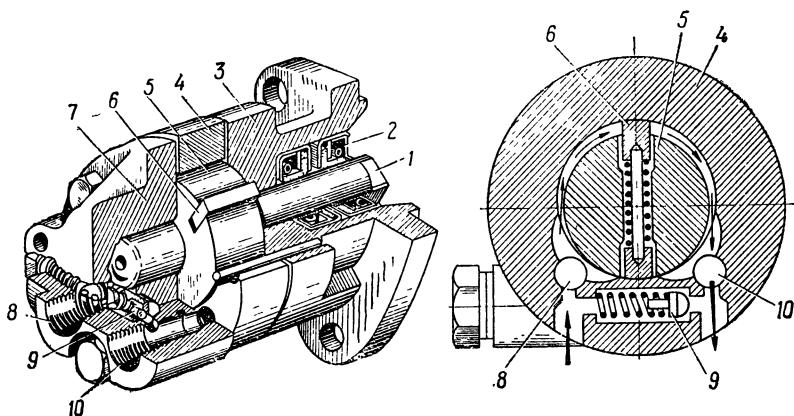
Топливоподкачивающий насос коловратного типа дизеля ЯАЗ-204:
